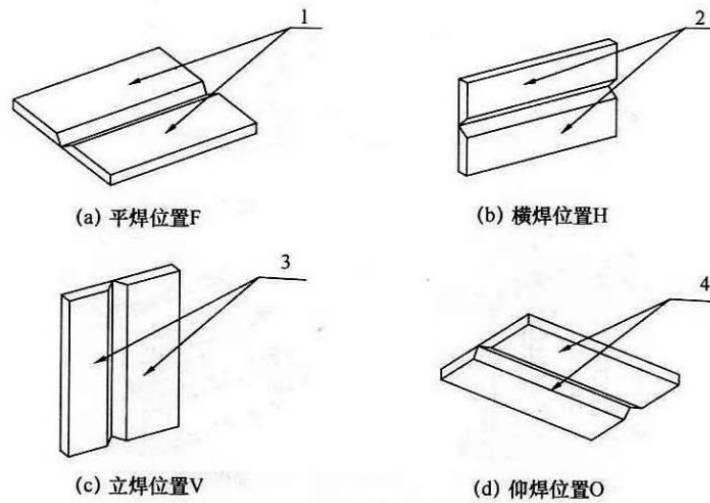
试板坡口焊缝焊接位置
